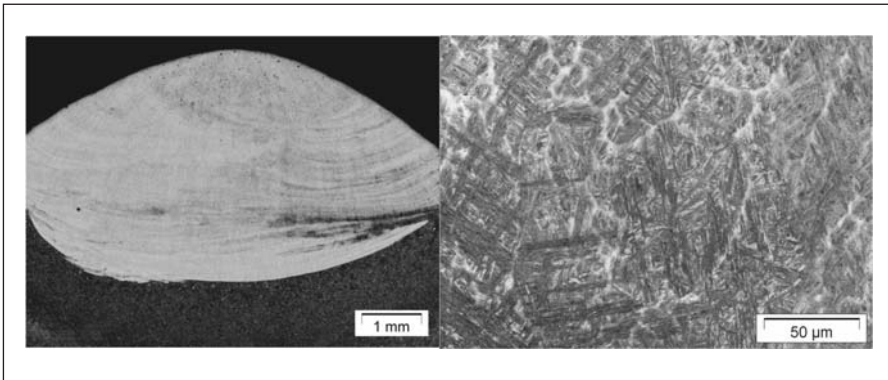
Schweißnahtgefüge des verwendeten Massivdrahtes
